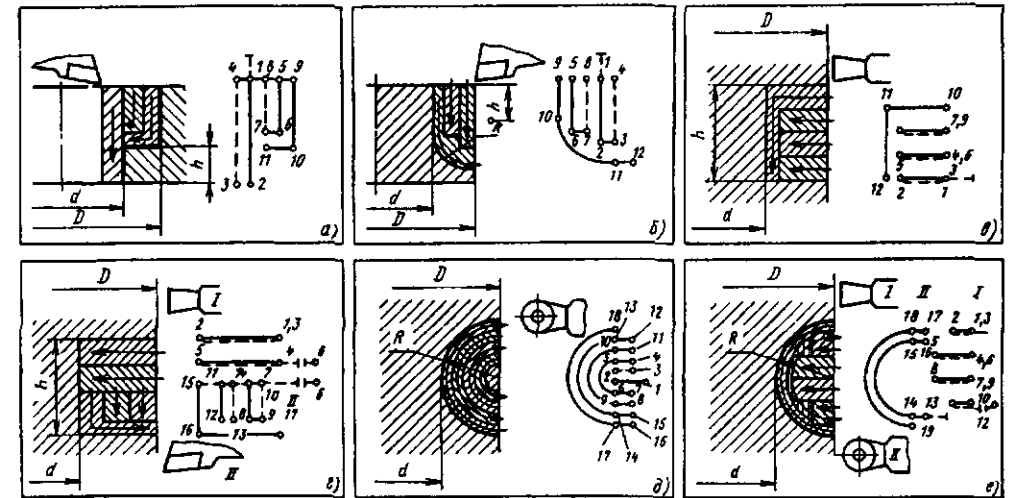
Схемы движения инструментов при снятии напусков на станке с ЧПУ в полукрытых (а и б) и в закрытых (с – е) зонах: D , d , h , R — выдерживаемые размеры
